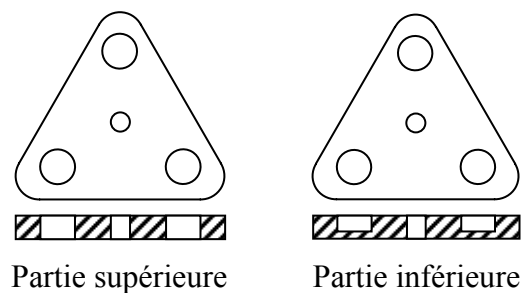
Porte éprouvettes des éprouvettes de résilience.
